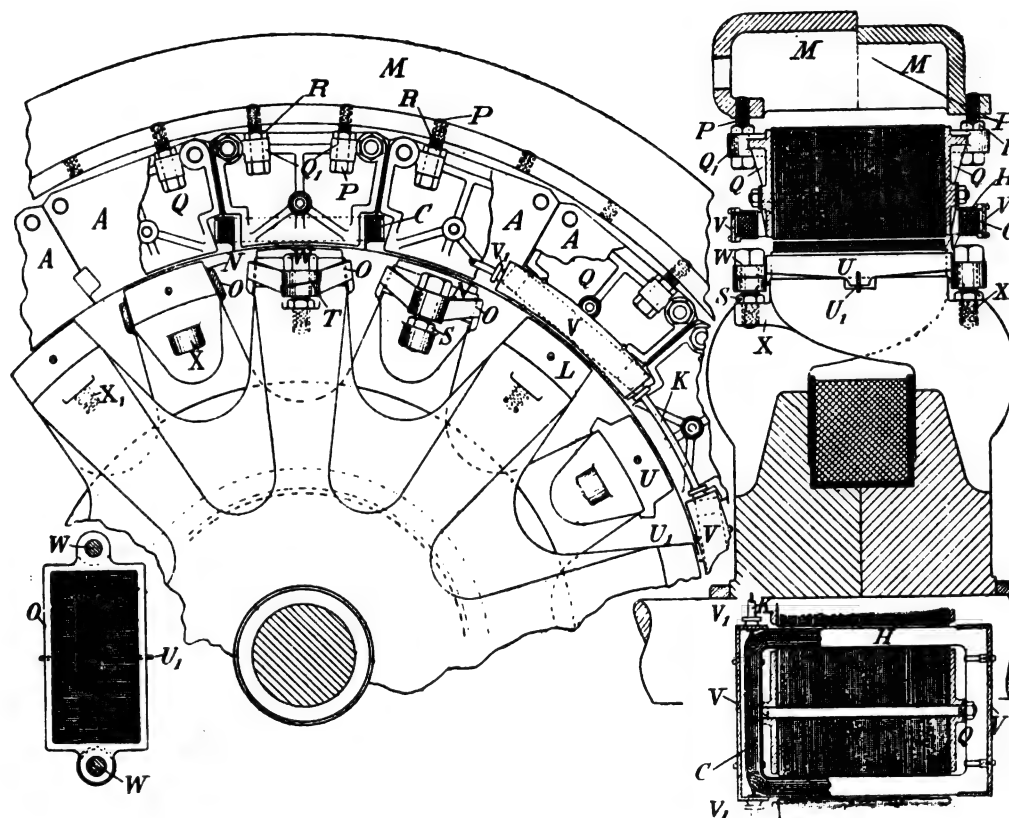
à 14. — Coupes et vues diverses d'un alternateur Johnson et Steele.
